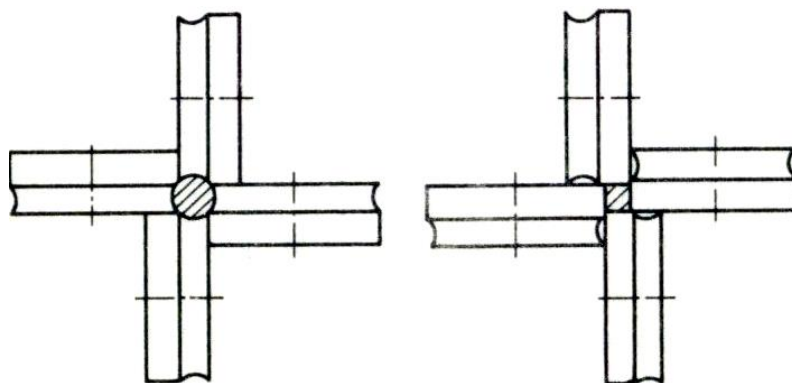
Сборка четырехвалковых калибров с размещением двух ручьев на бочке каждого валка
